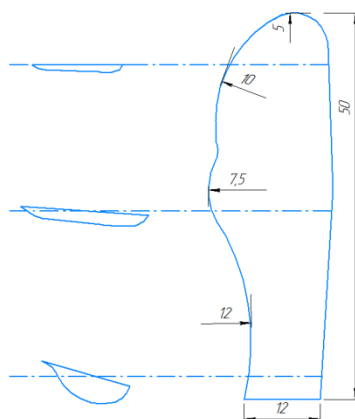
Примерный чертёж лопасти в форме кленовой крылатки согласно руководству.
